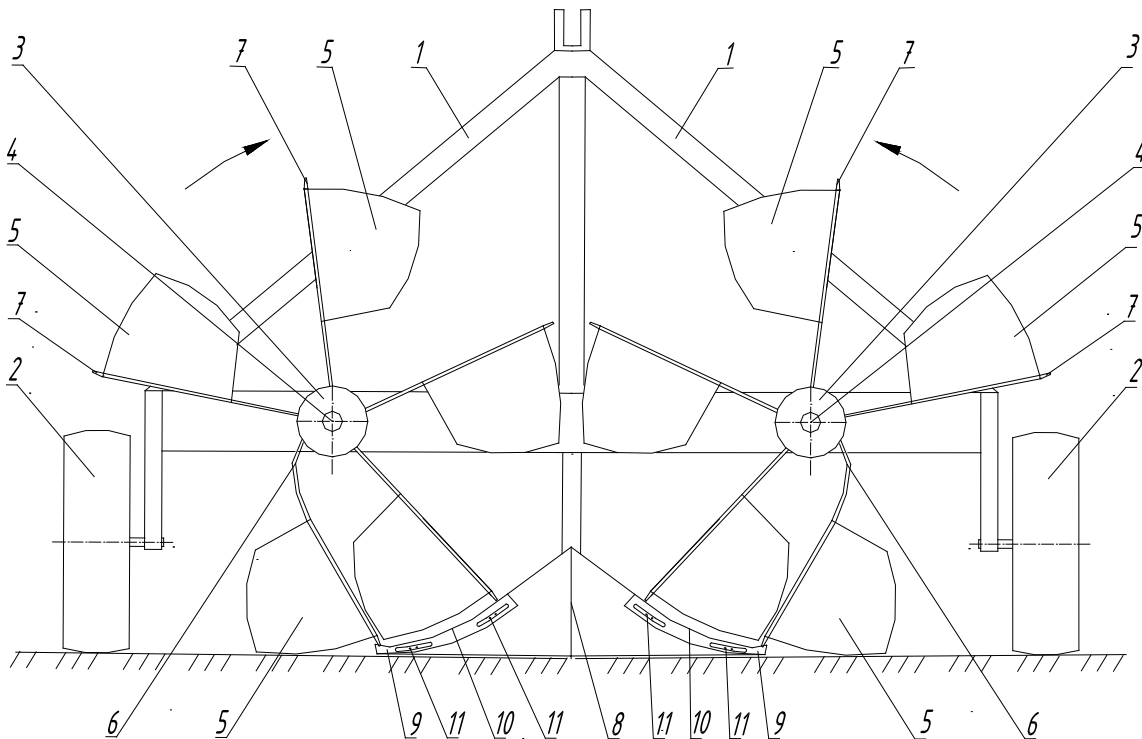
Схема роторного розкидача органічних добрив: 1 – рама; 2 – колеса; 3 – маточини; 4 – привідний вал; 5 – лопать; 6 – пружина; 7 – виступ; 8 – дільник; 9 – поріг; 10 – робоча поверхня порога; 11 – механізм зміни положення порогів
